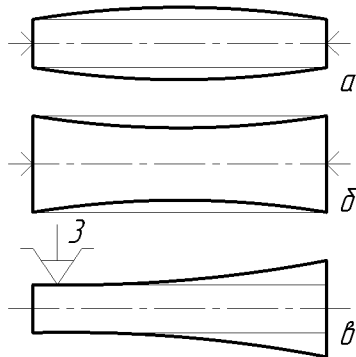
Похибки форми при обробці на токарному верстаті:
